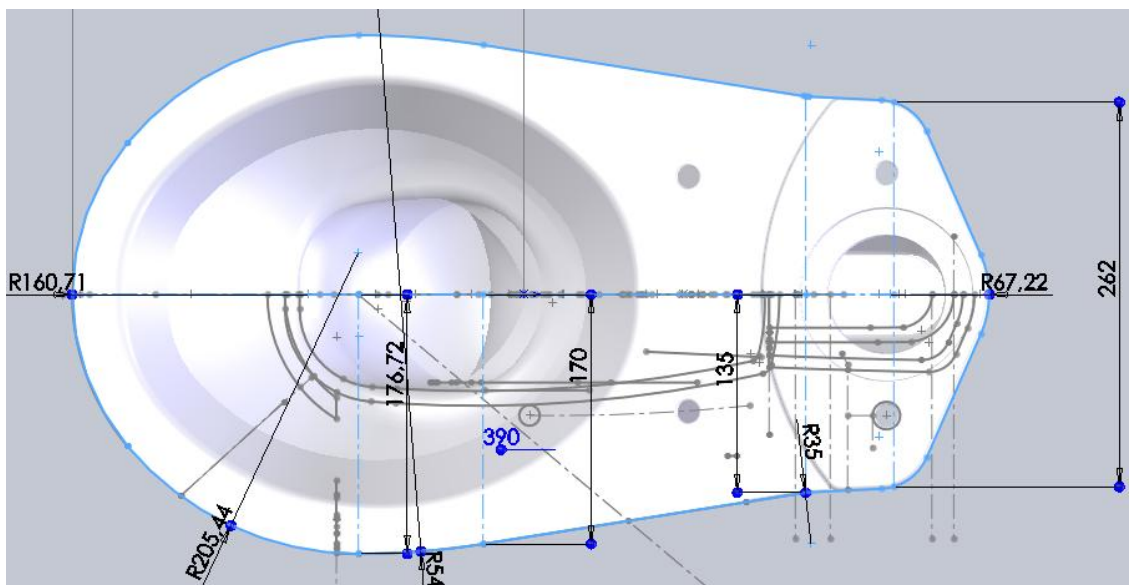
Croquis en SolidWorks de la planta de la taza
